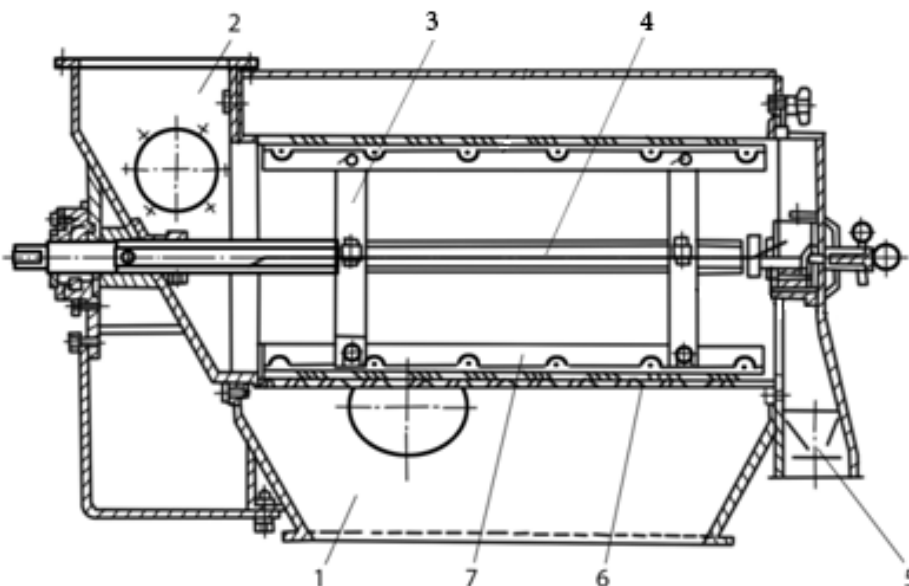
Просеиватель: 1 - корпус; 2, 5 - приемный и выпускной патрубки; 3 - бич; 4 - ротор; 6 — ситовой цилиндр; 7 — очиститель.
